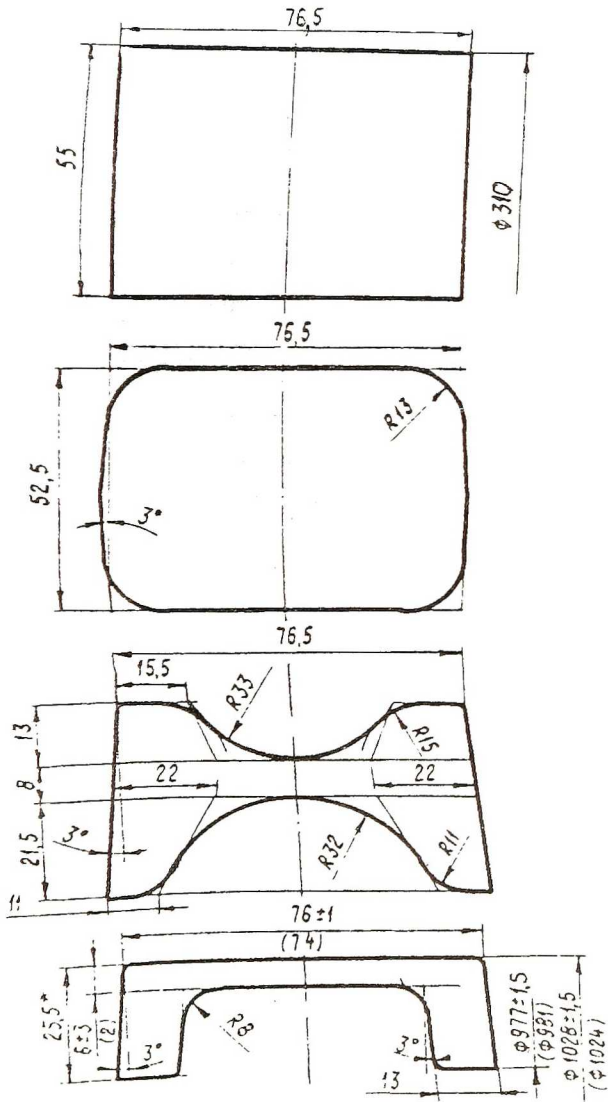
Калибровка заготовок промежуточного кольца компрессора из сплава ВТ20
